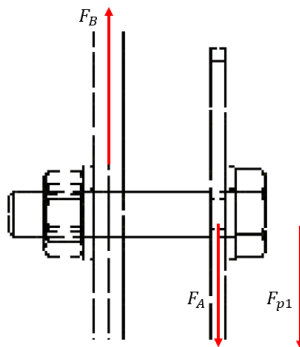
Esfuerzo cortante en el tornillo AB. (Fuente propia).
